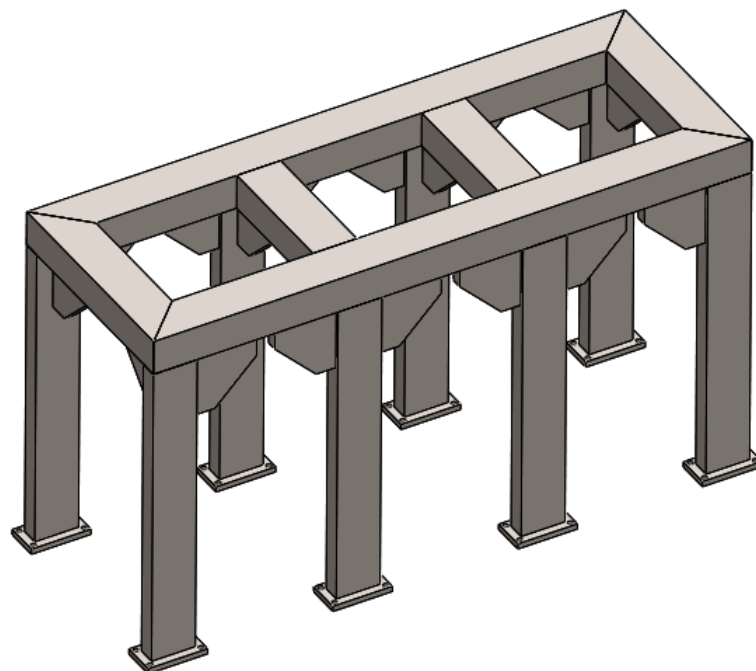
Estructura del soporte del bastidor (columnas y vigas)
